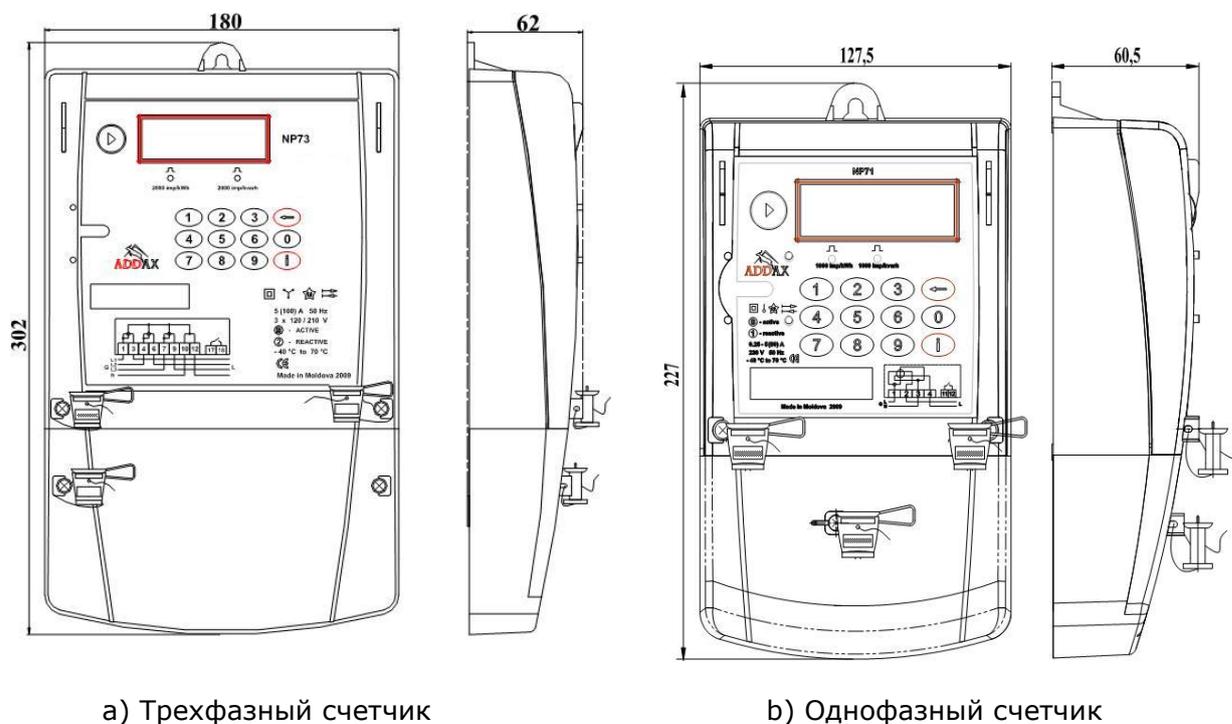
Общий вид и габаритные размеры счетчика со стандартной крышкой клеммника
